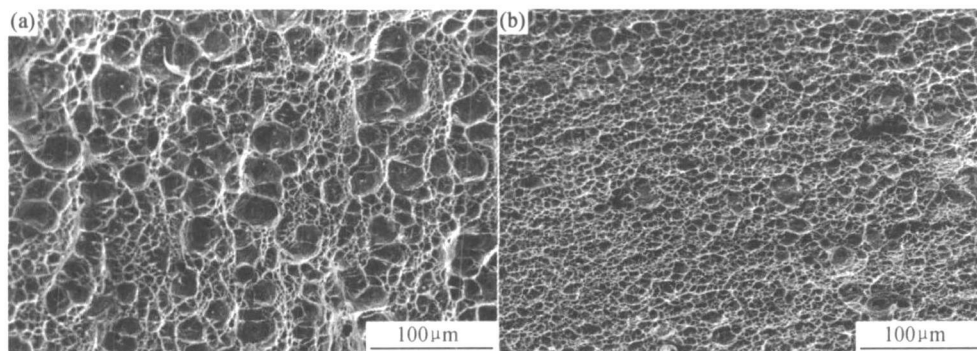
拉伸断口扫描电镜照片 (a) GTAW 焊接接头; (b) 母材
